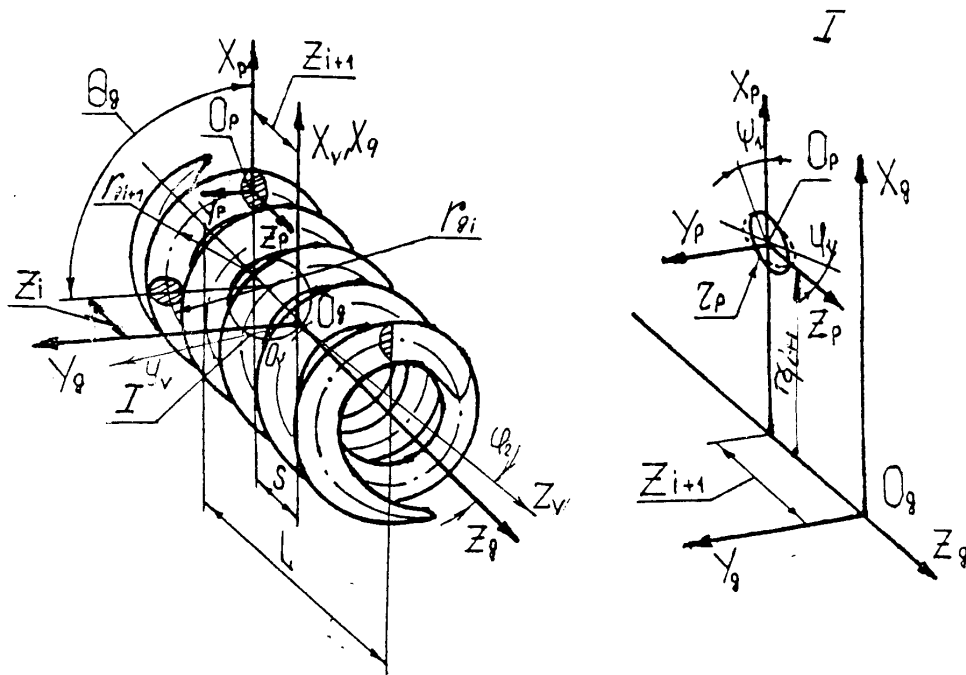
Рассчётная схема для описания поверхности цилиндрической пружины.
